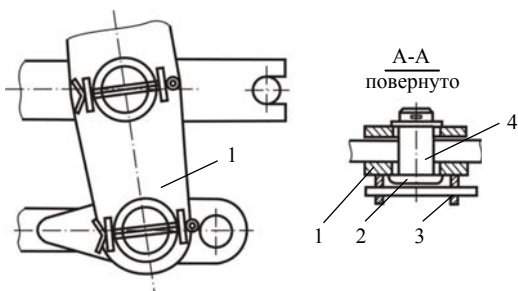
Установка предохранительного шплинта валика вертикального рычага
